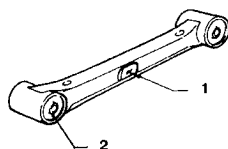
Расположение цветовой метки на поперечной тяге (См. Раздел 9)
